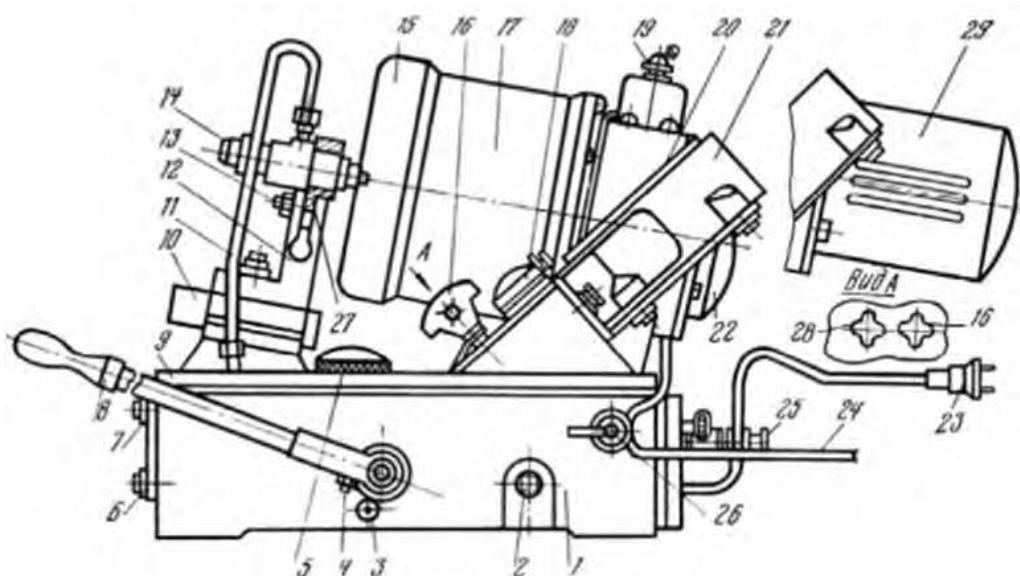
Прибор КИ-3333 для регулировки и испытания форсунок:
